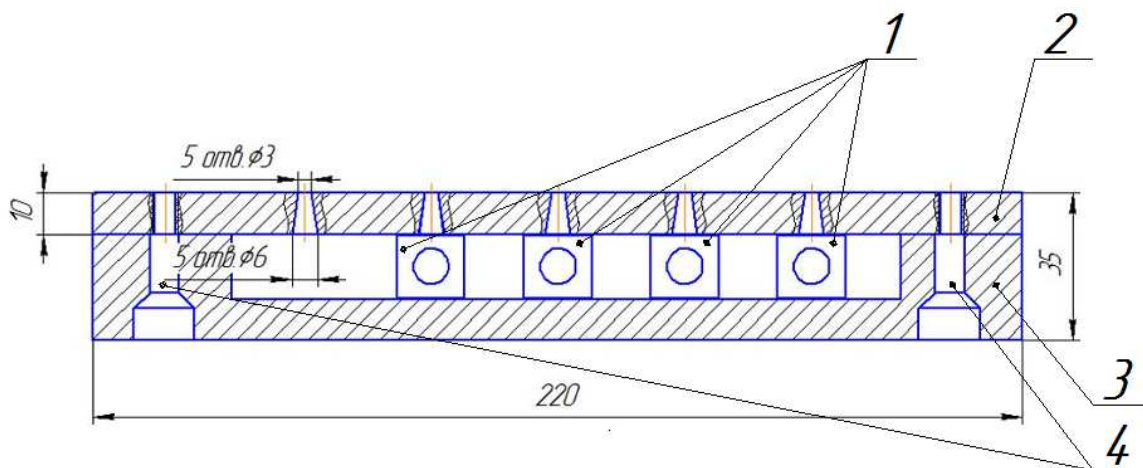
Блок-образец. 1 – Штифты; 2 – Поверхность для нанесения покрытия; 3 – корпус; 4 – Винты.
